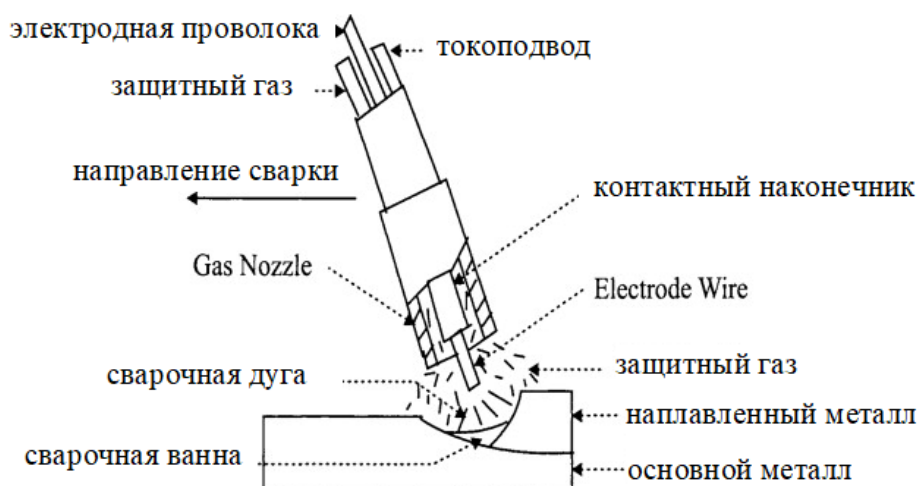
Схема механизированной сварки в защитном газе проволокой сплошного сечения
